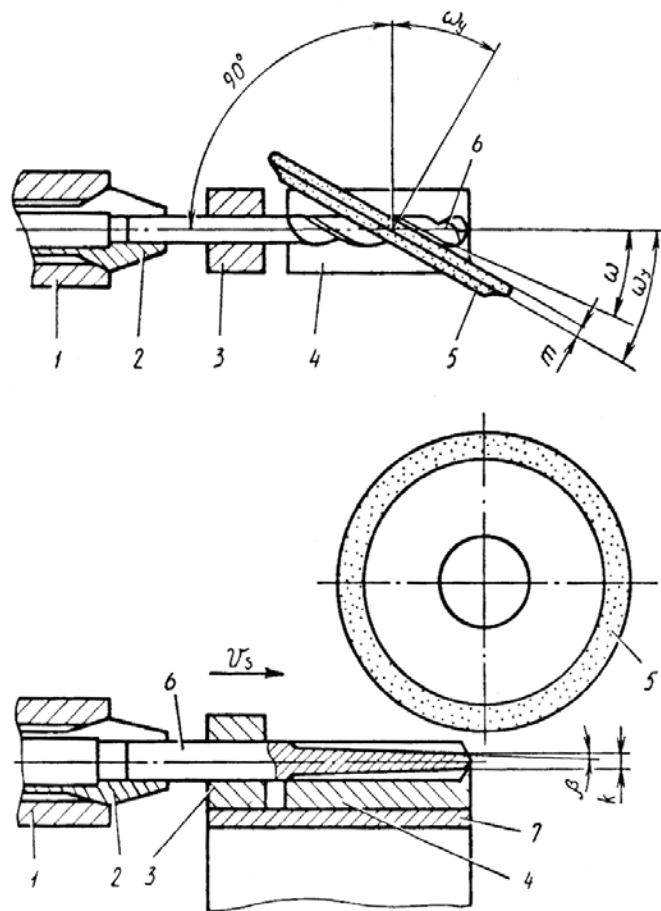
Расположение заготовки и абразивного инструмента при вышлифовке канавок инструмента:
